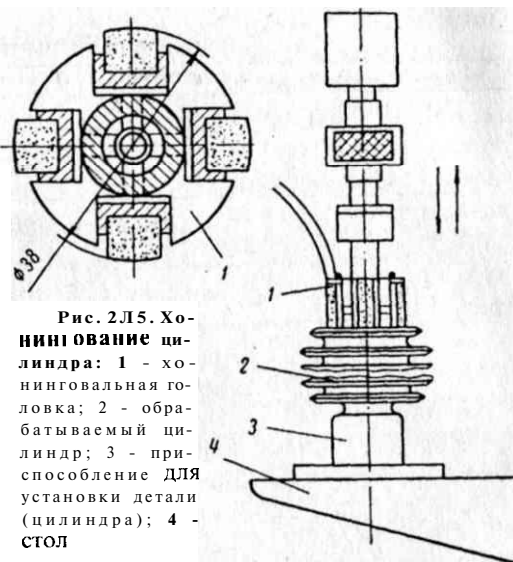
Хонингование цилиндра: 1 - хонинговальная головка; 2 - обрабатываемый цилиндр; 3 - приспособление для установки детали (цилиндра); 4 - стол
